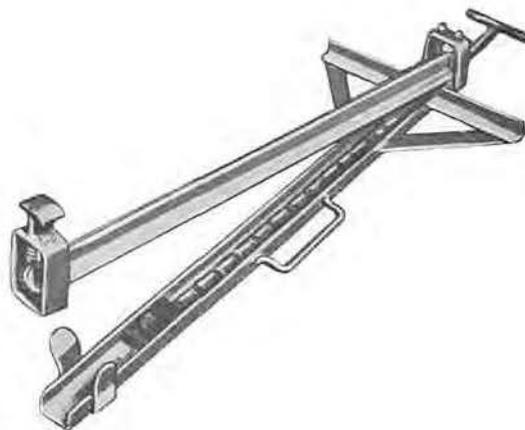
Machine «Comet» à couper les courroies. La bande se place entre la glissière inférieure et la double cornière supérieure.
